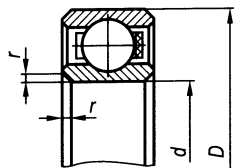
Подшипник шариковый радиальный однорядный гибкий
